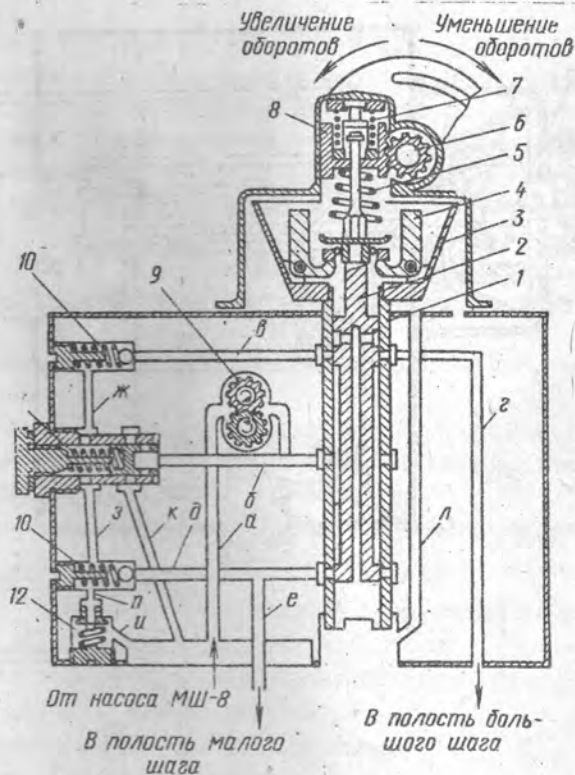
Схема устройства регулятора оборотов Р9-СМ2: 1-воздушный валик; 2-золотник; 3-колокол; 4-Г-образные грузики; 5-коническая пружина; 6-валик ручного управления с шестерней; 7-балансирующая пружина; 8-зубчатая рейка; 9-насос регулятора; 10-шариковые клапаны; 11-редукционный клапан; 12-перегрузочный клапан
